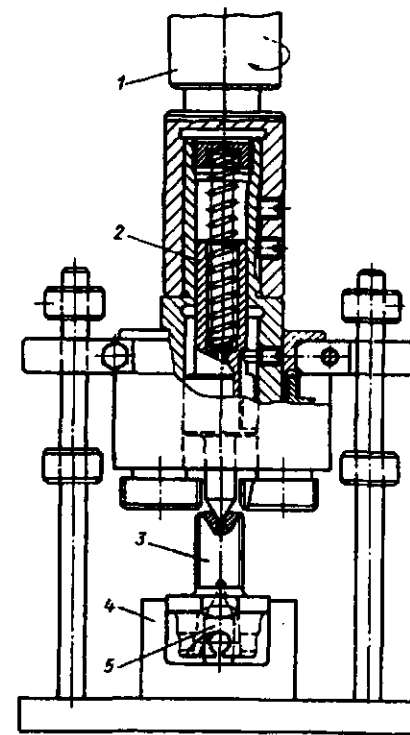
Схема нарезания наружной резьбы головкой с пружинным центром: 1 – шпиндель станка; 2 – пружинный центр; 3 – нарезаемая деталь; 4 – приспособление; 5 – нижний центр
